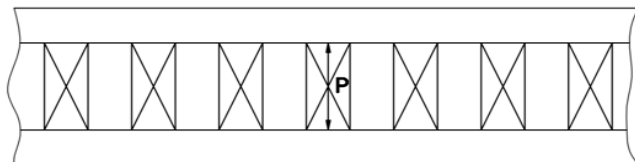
Схема разжима полков сварной станины суппортов станка
